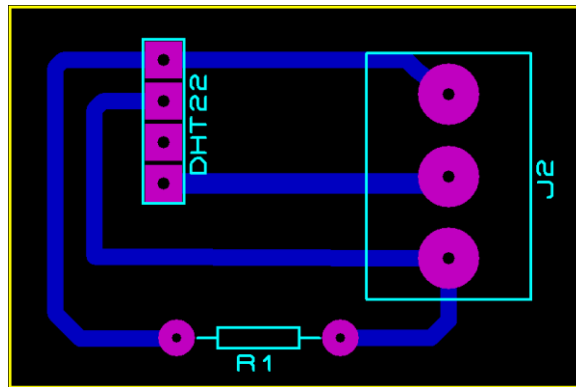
Diseño de Circuito Impreso para Sensores DHT-22
